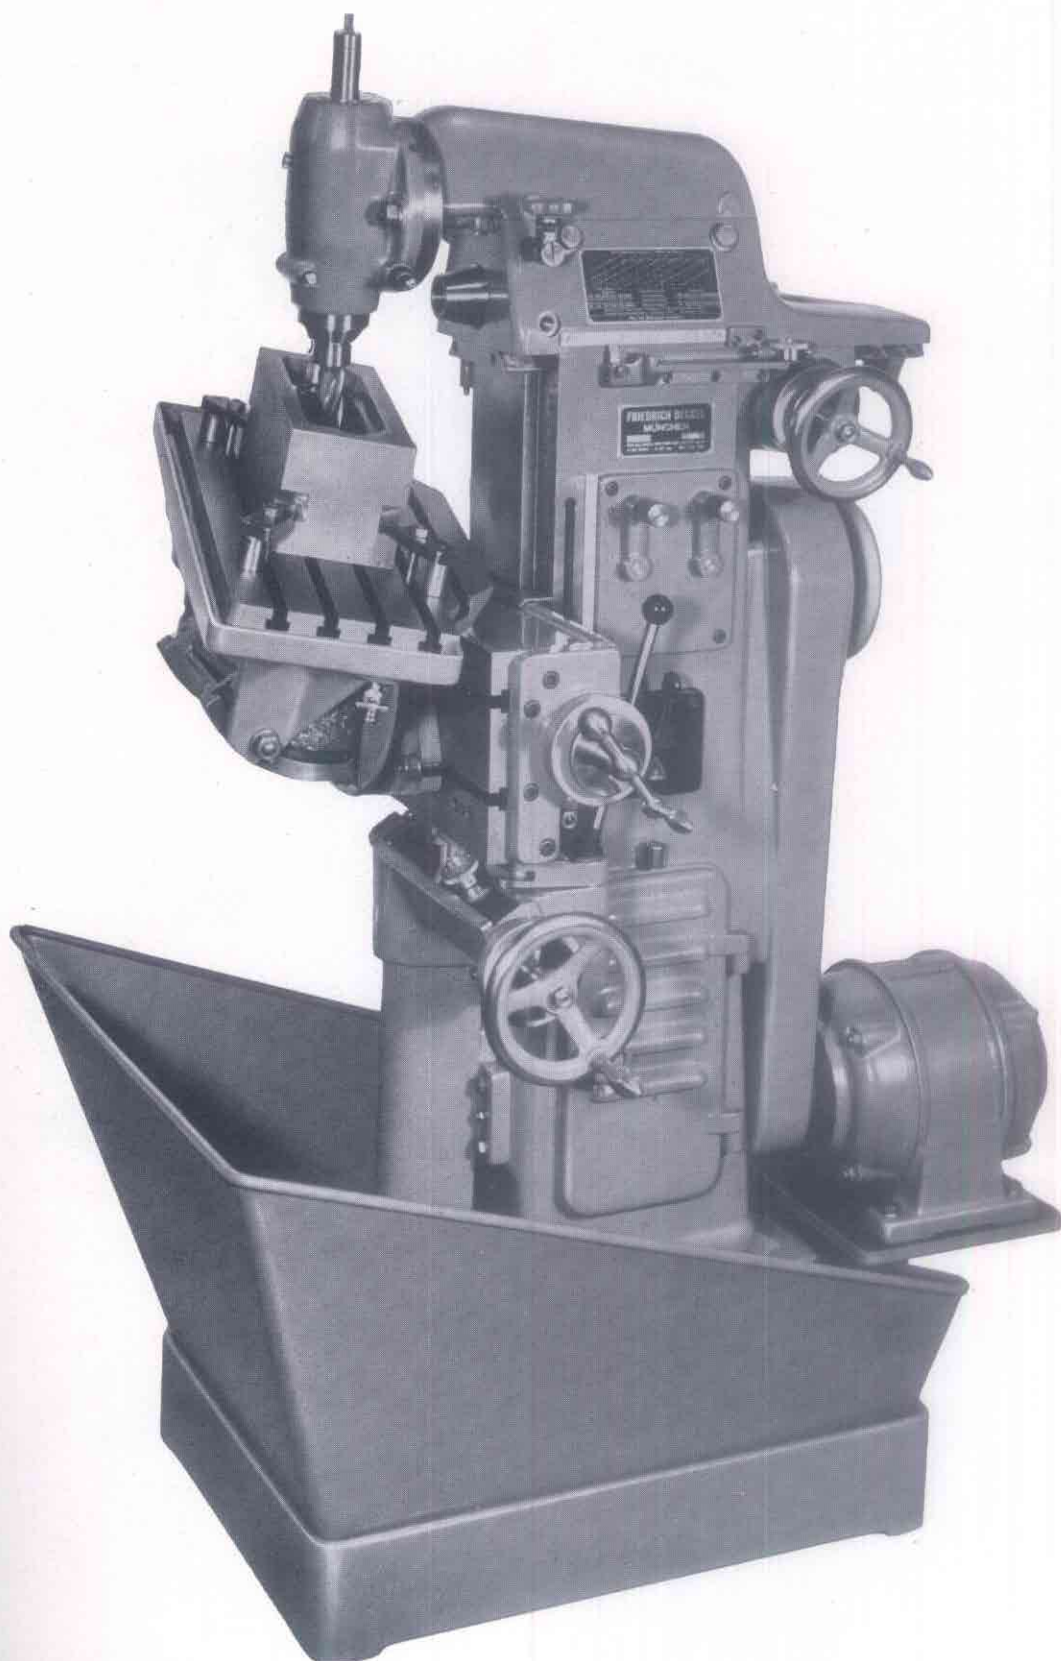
Universal-Werkzeug-Fräsmaschine FP 1
